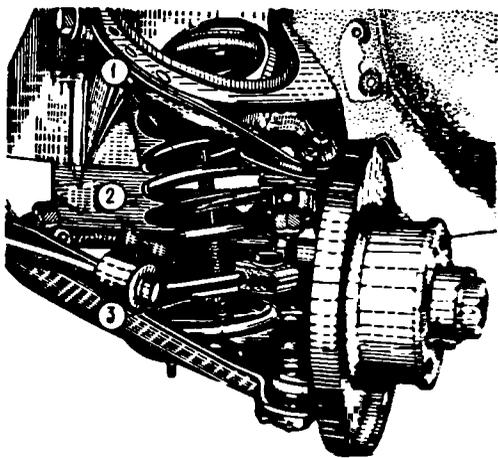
Сжатие пружины приспособлением 67.7828.9504: 1 - пружина подвески; 2 - винт приспособления; 3 - опорная тарелка
